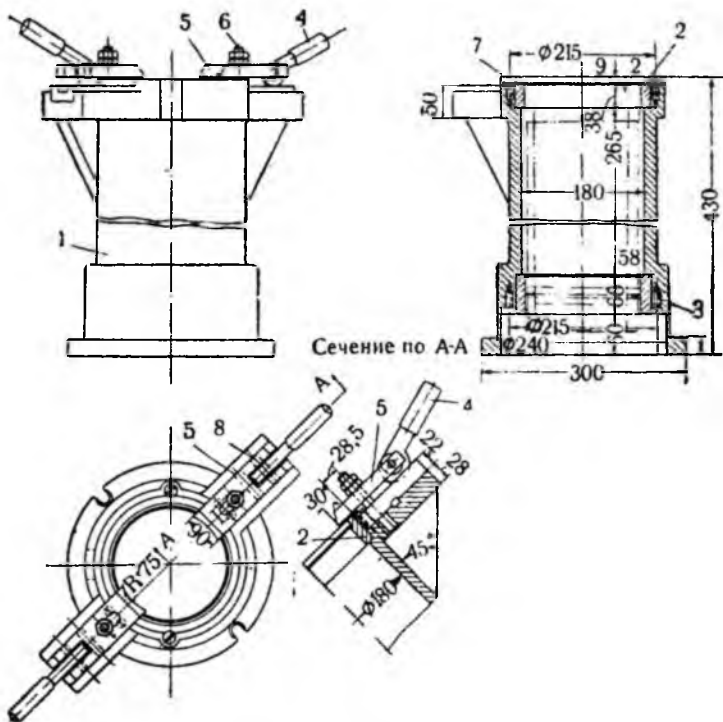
Приспособление для крепления гильз ЧТЗ-С-65 на расточном и шлифовальном станках:
